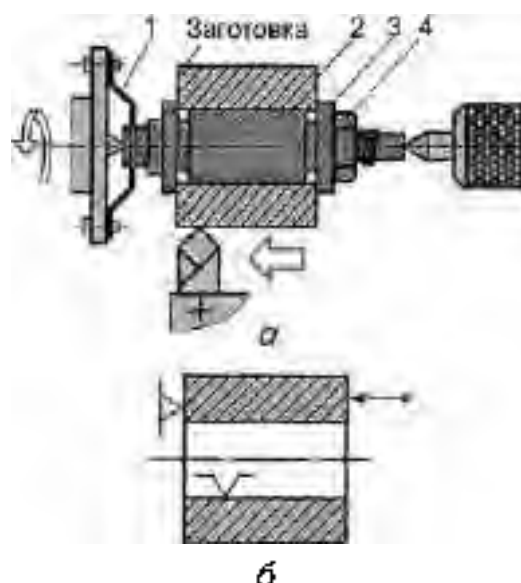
Закріплення заготовки втулки на циліндричній оправці (а) та умовне позначення (б):
